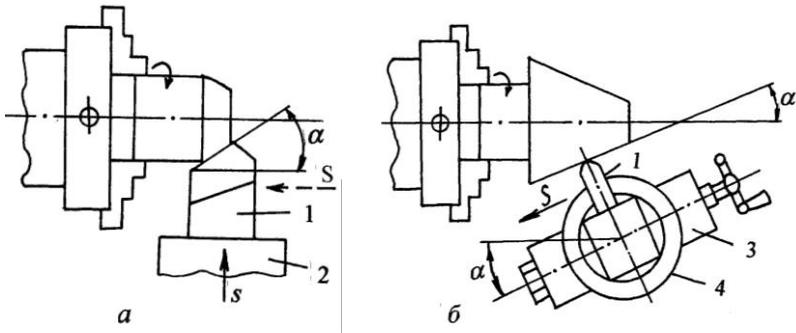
Схемы обработки конических поверхностей на токарно-винторезных станках:
